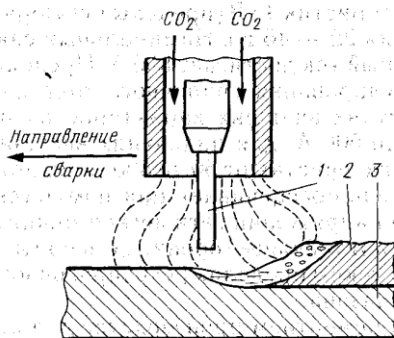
Схема сварки (наплавки) в среде углекислого газа:
